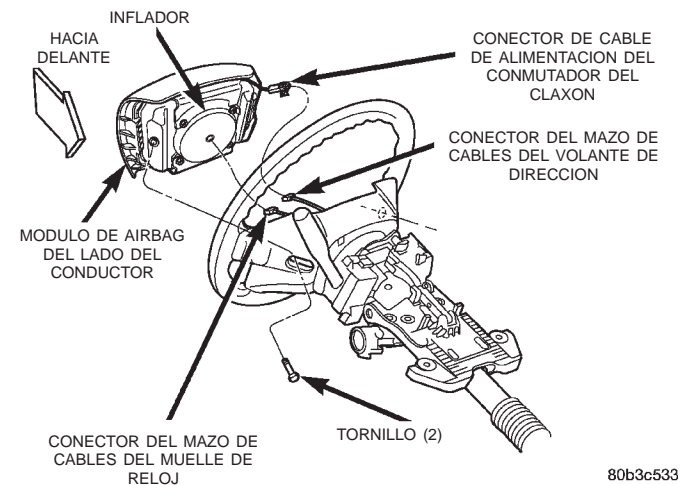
Desmontaje e instalación del módulo de airbag del lado del conductor
